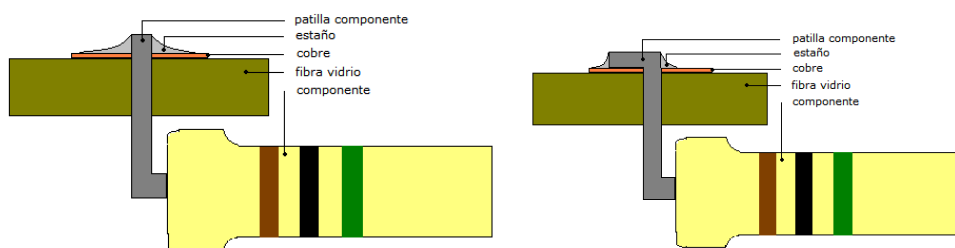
Soldadura cóncava para una patilla de resistencia
